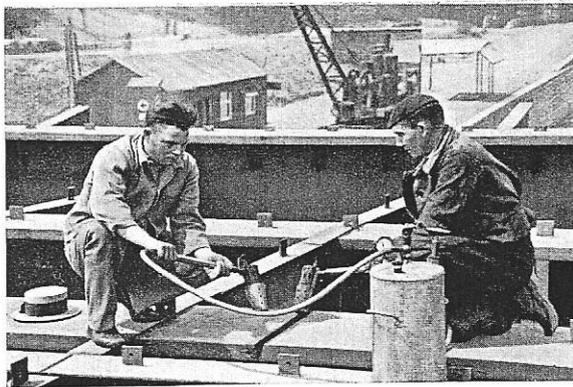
Préchauffage d'un joint en V avant soudure.
